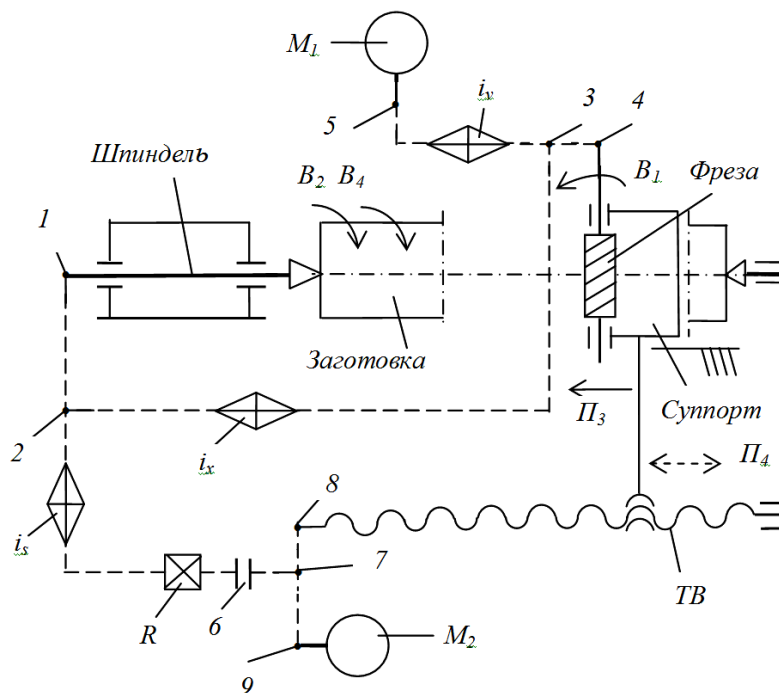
Бездифференциальная структурная схема шлице-зубофрезерного станка
